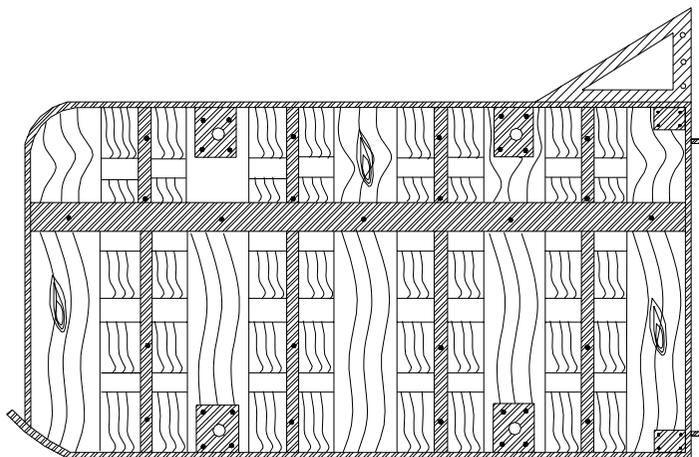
Portón Rectangular Plano de Acero y Madera para Arrastre de Camarón
